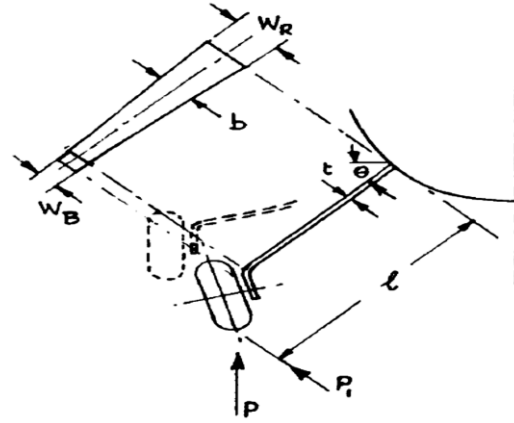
Pierna del tren de aterrizaje como una viga en cantiléver de sección transversal rectangular y espesor constante.
